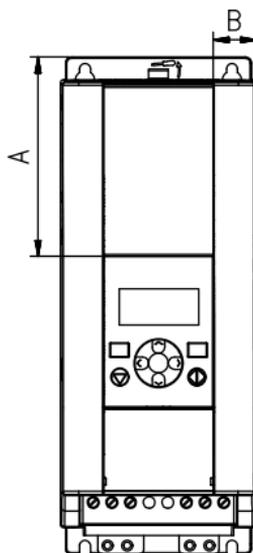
Dimensões do Praxi 10, MI2 - 3 Local de Visor
